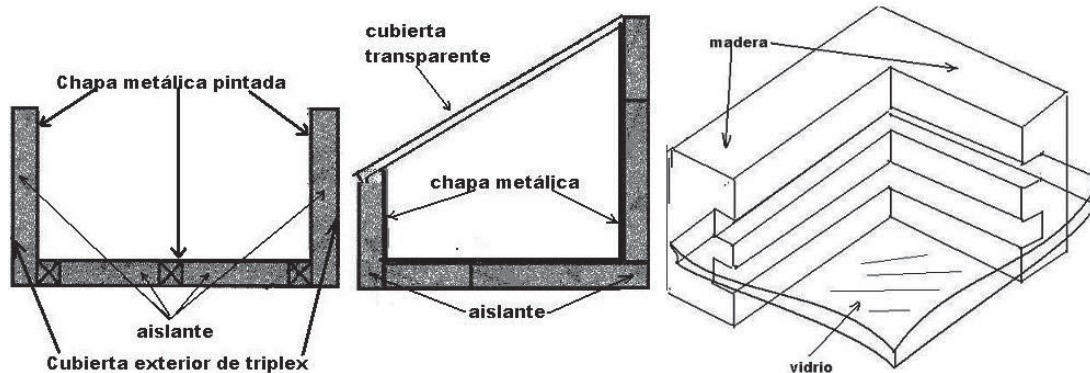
Estructura de las cocinas y detalle de la cubierta transparente.
